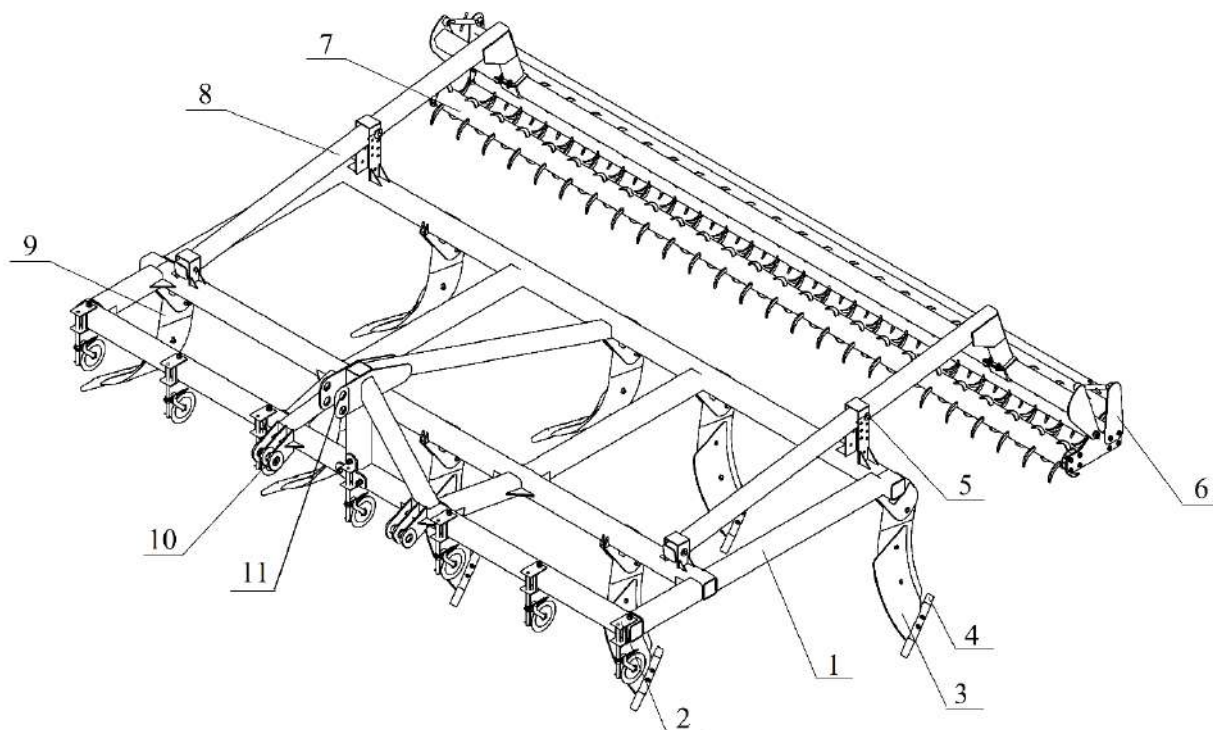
Агрегат для глибокого розпушування ґрунту: 1- рама; 2 – дисковий ніж; 3 – глибоко розпушуюча лапа ; 4 – долото; 5 – опора катка; 6 – корпус катка; 7 – каток; 8 – кронштейн катка; 9 – кронштейн лапи; 10 – навіска; 11 – навіска.
